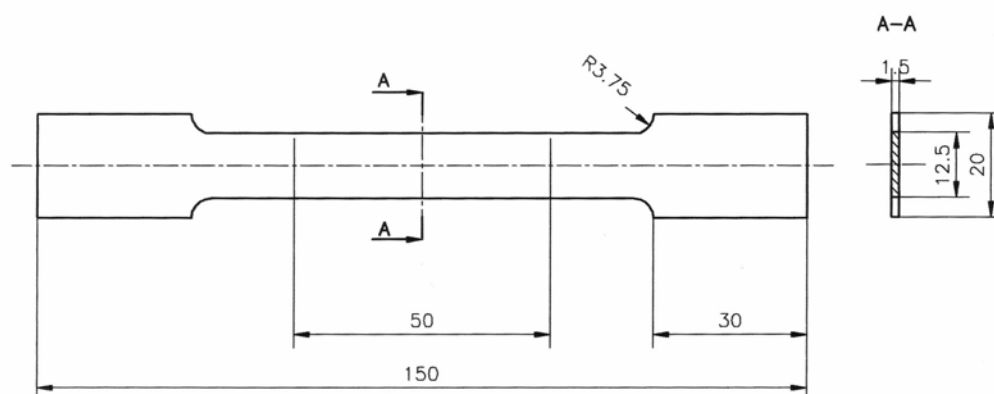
Geometria e dimensões do provete para ensaio de tracção.
